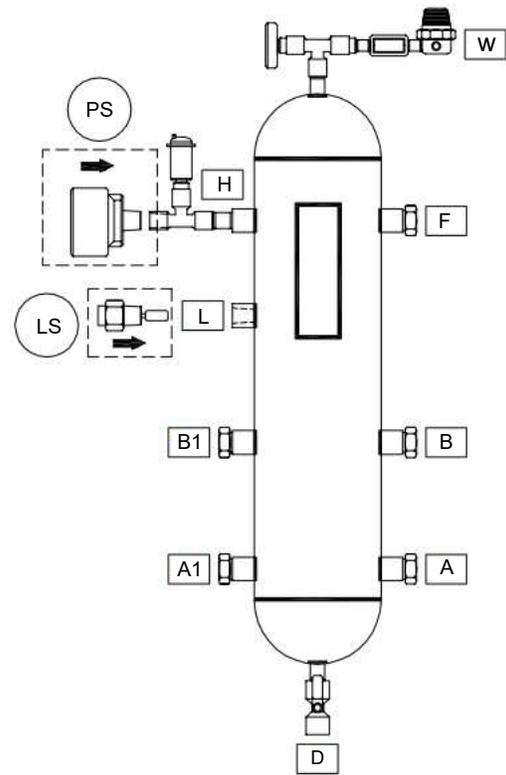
Montaje de interruptores del Plano 53A WM de tuberías
